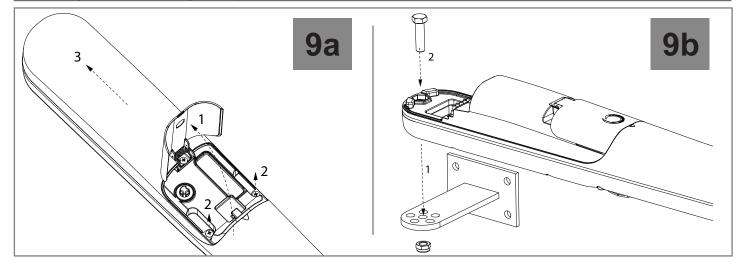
IT - Fissaggio motoriduttore e staffa anteriore
